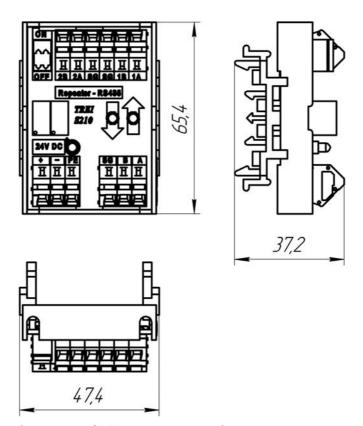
Чертеж общего вида S210 с указанием габаритных и присоединительных размеров
